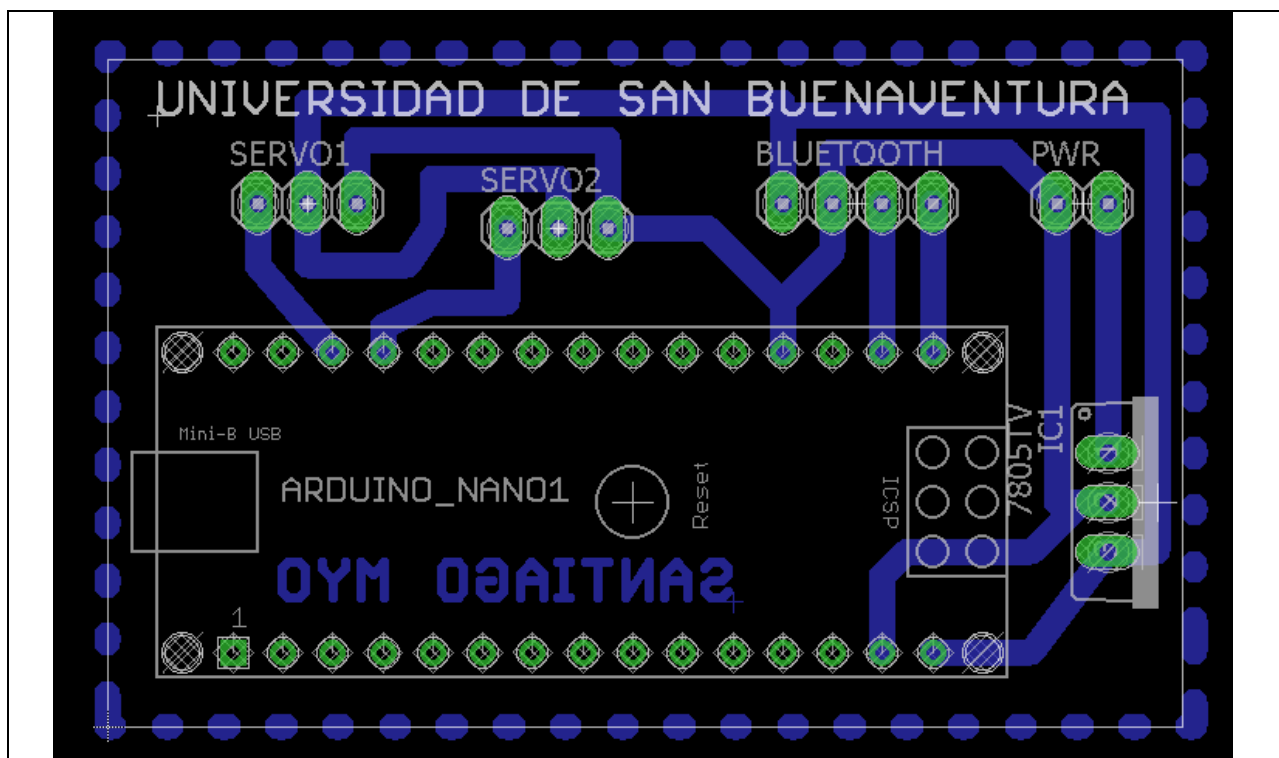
Diseño PCB de la tarjeta controladora del prototipo de prótesis.
